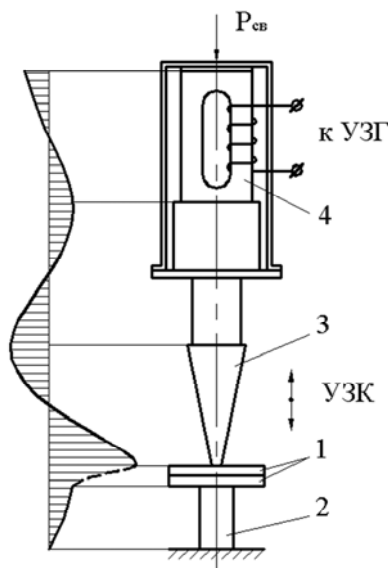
Схема ультразвуковой сварки пластмасс:
